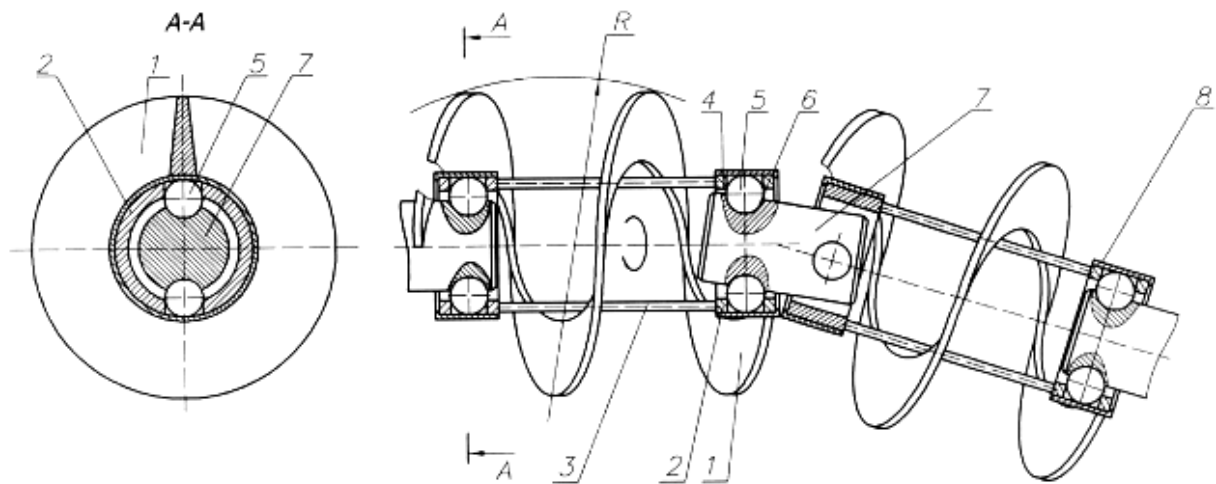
Конструктивна схема гвинтового секційного робочого органу транспортера
